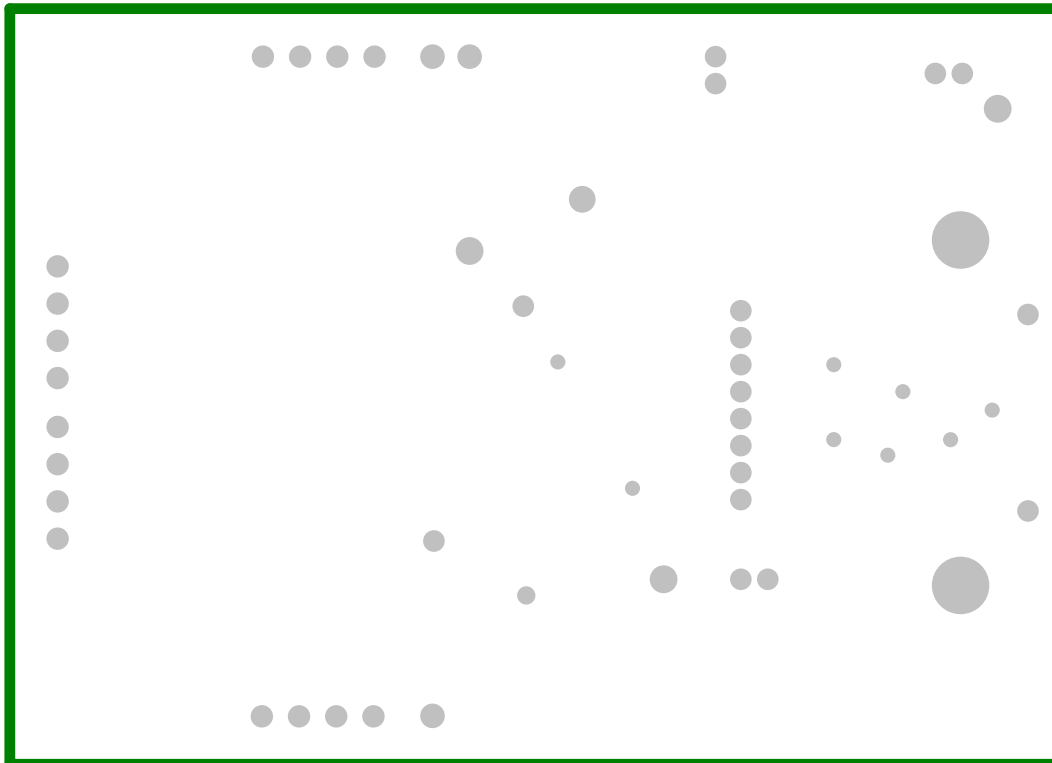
ADS125P08 評価基板 PCB レイアウト — グランド層 1
